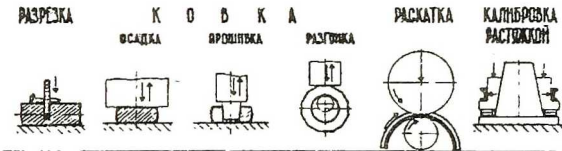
Технологическая схема получения колец раскаткой из кованой заготовки
